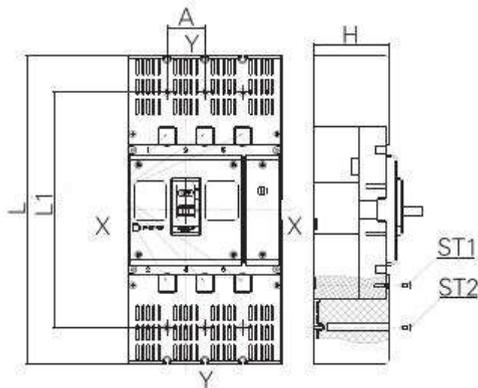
Габаритные размеры крышек клеммника длинных КК-300Rc
